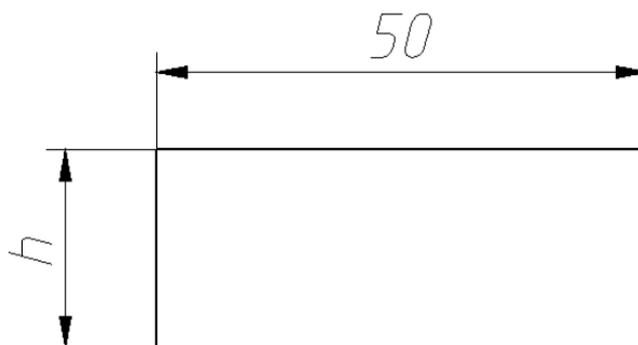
Имитатор усиления сварного шва; h – толщина
